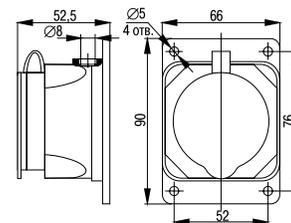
Розетка (колодка) двухместная с защитными крышками РКП16-002
